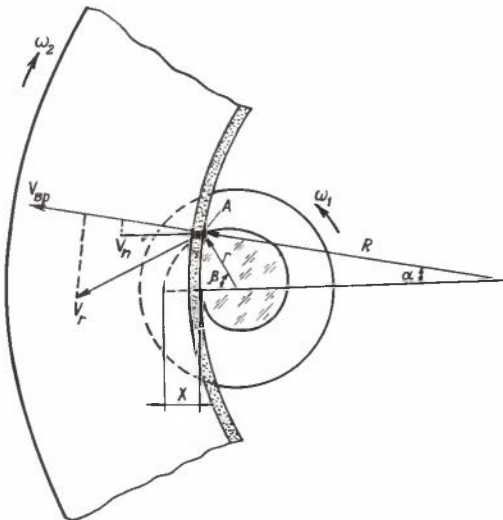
Схема резки вращающегося кристалла алмазным диском с внутренней режущей кромкой
